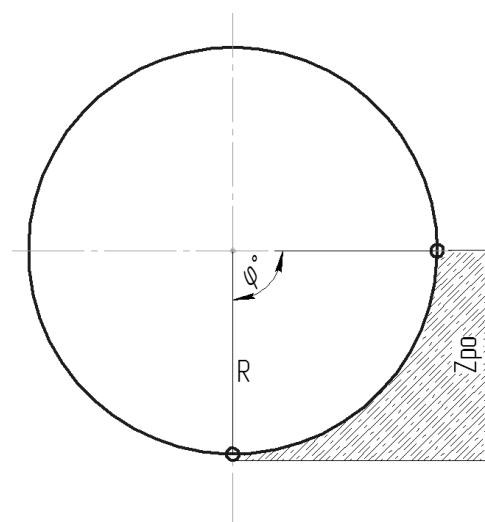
Определение угла контакта фрезы с обрабатываемой средой
